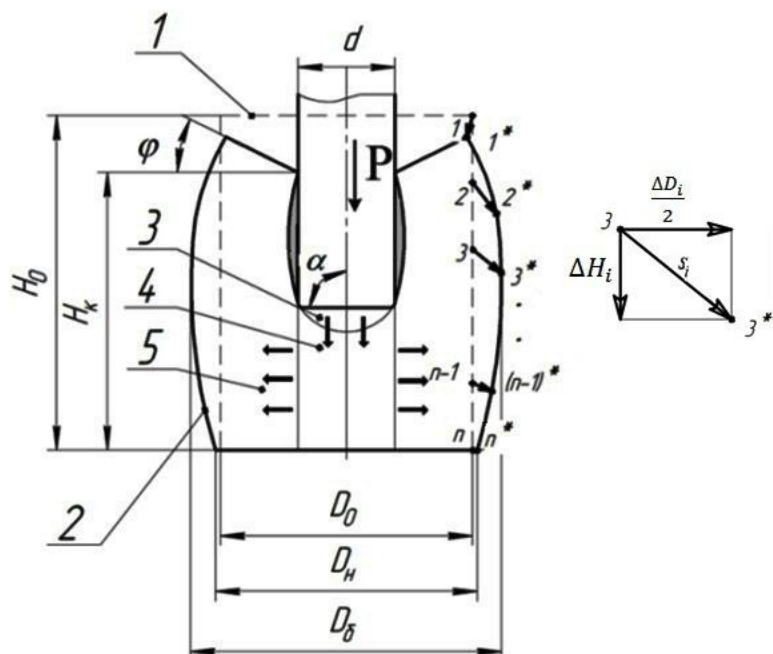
Анализ формоизменения цилиндрической заготовки при открытой прошивке
